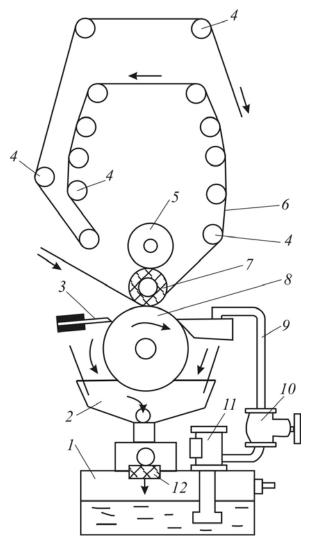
Секция глубокой печати: 1 — резервуар с краской; 2 — корыто; 3 — ракель; 4 — направляющие валики; 5 — пресс-цилиндр; 6 — запечатываемая лента; 7 — печатный цилиндр; 8 — формный цилиндр; 9 — трубопровод; 10 — вентиль; 11 — насос; 12 — фильтр
